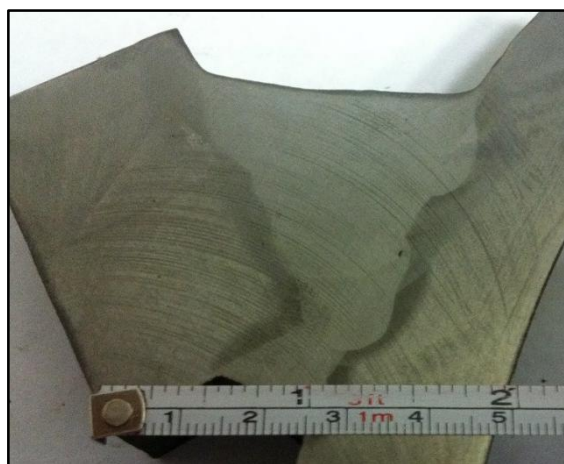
Sección transversal de la unión soldada de la placa y el cilindro de suspensión.
